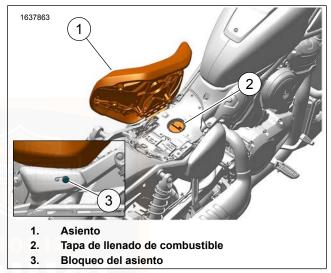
Llenado de combustible (tanque de combustible debajo del asiento)
